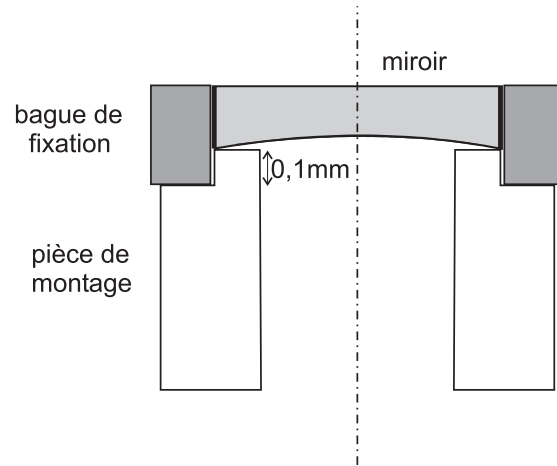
Vue en coupe de la pièce utilisée pour le montage de la cavité.
